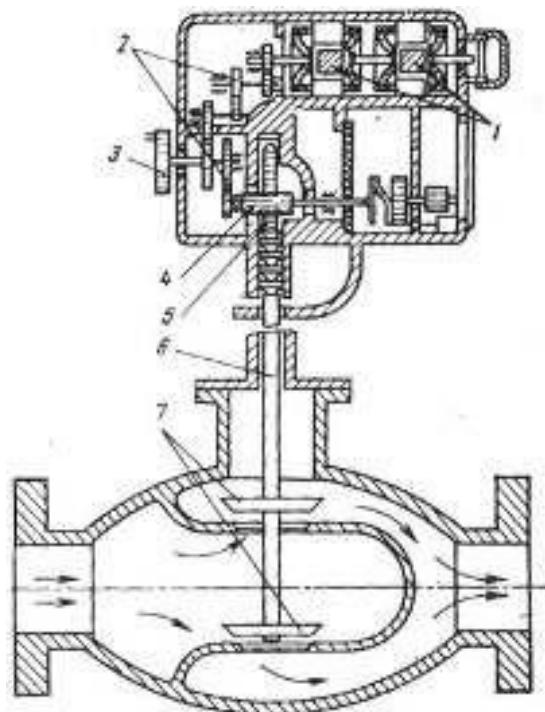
Кинематическая схема электродвигательного исполнительного механизма
